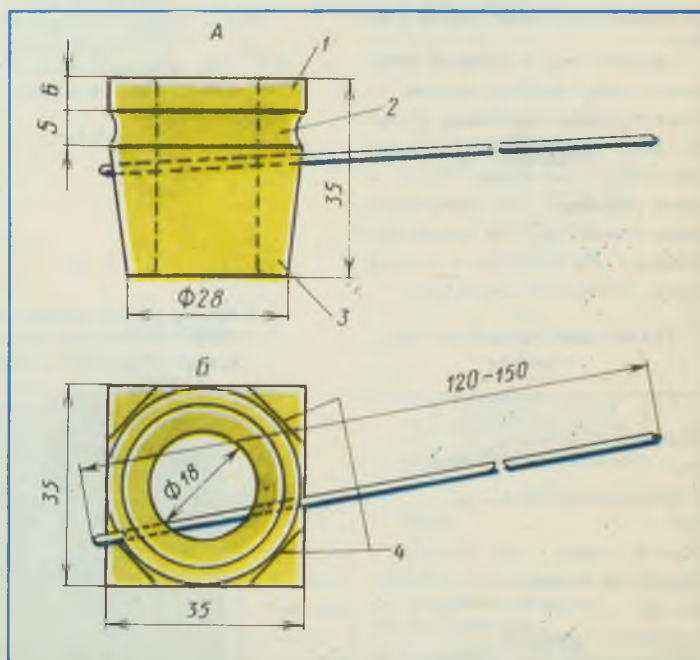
Общий вид удильника: А — вид сбоку; Б — вид снизу; 1 — квадратный фланец; 2 — кольцевая канавка; 3 — конус; 4 — надрезы.
